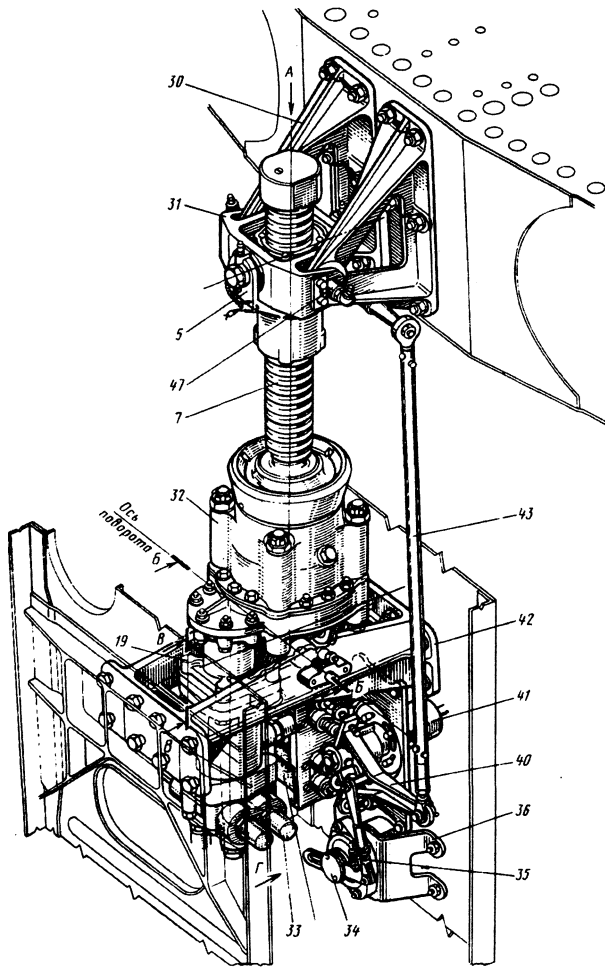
Механизм перестановки стабилизатора (общий вид)
